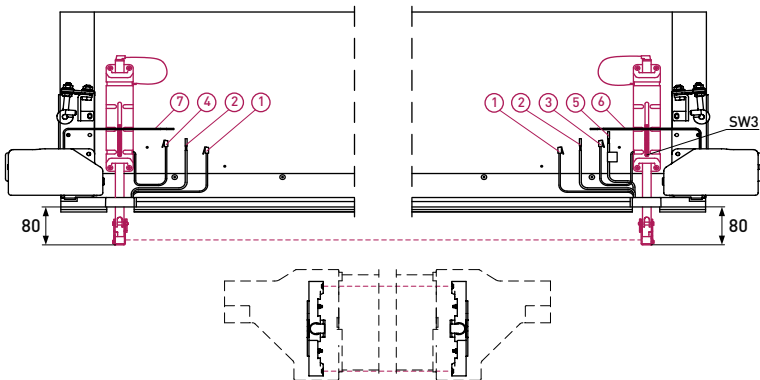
Einrichtung der Stangeposition mit dem Sensor des Sets PFS-200KIT
